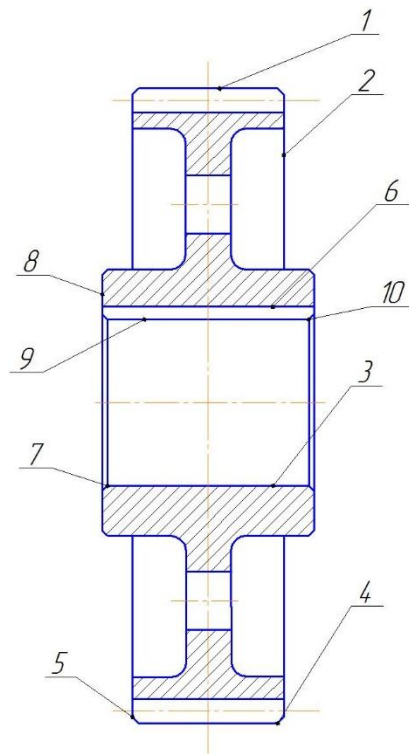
Ескіз деталі «Шестерня 600.005.04»
